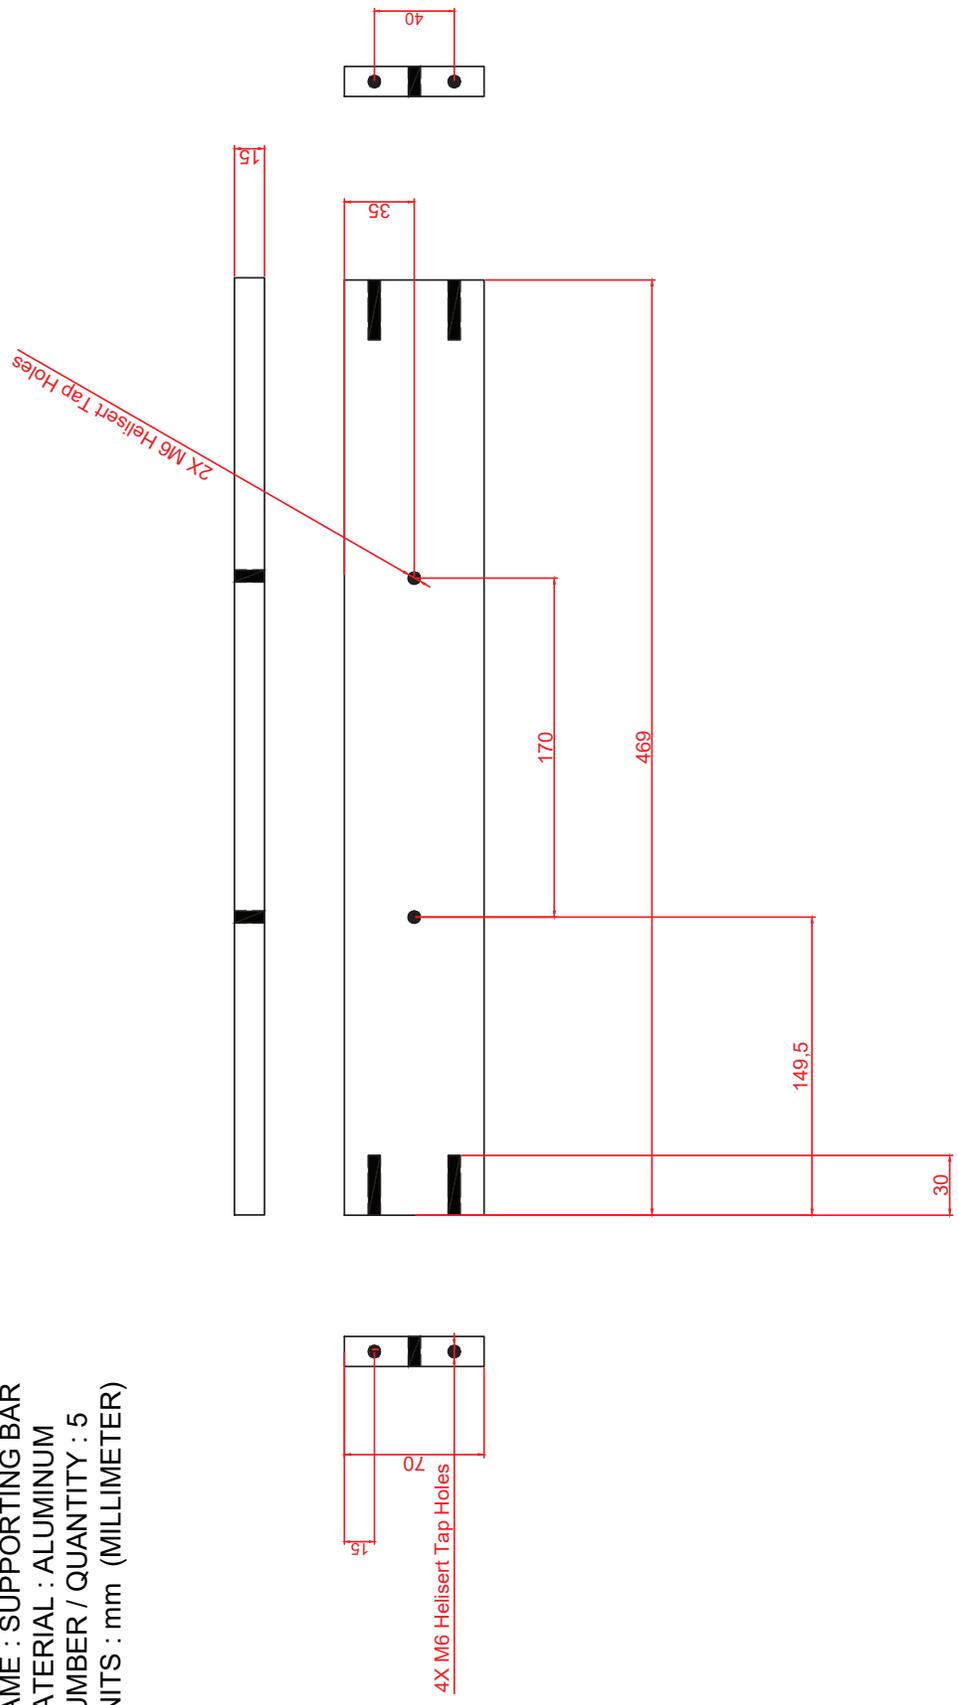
サポート板の概要図。全てのタップ穴はヘリサート加工されることを希望する。 / Schematic drawing of the supporting bar. All tapped holes should be heliserted.
